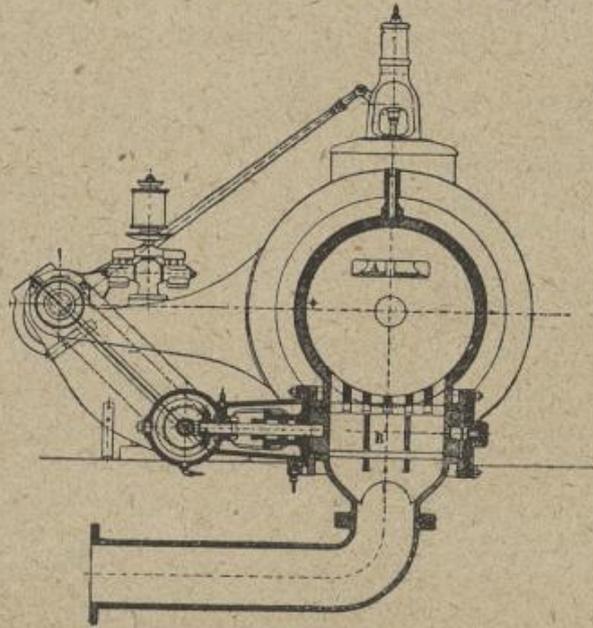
Machine équicourant Smal ; coupe transversale.
